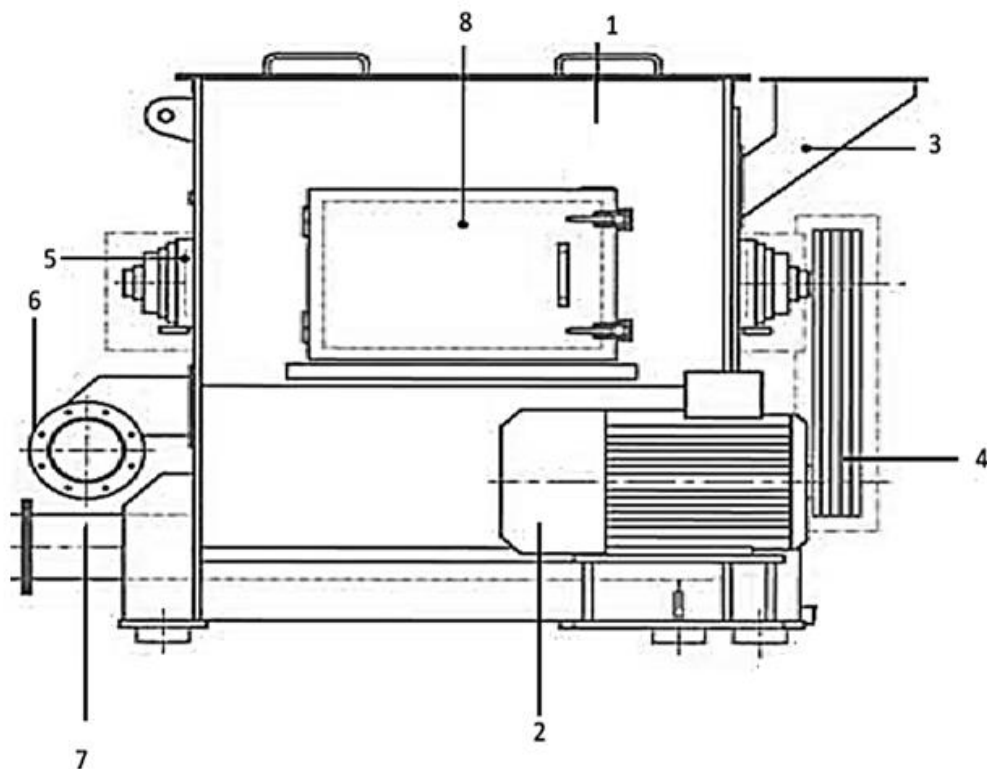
Схема центрифуги з позначенням деталей: 1 – корпус , 2 – електродвигун 3 – завантажувальний бункер, 4 – клинові ремені, 5 – підшипникові вузли 6 – вивантажувальний клапан, 7 – патрубок зливу рідини та забруднень, 8 – оглядовий люк
